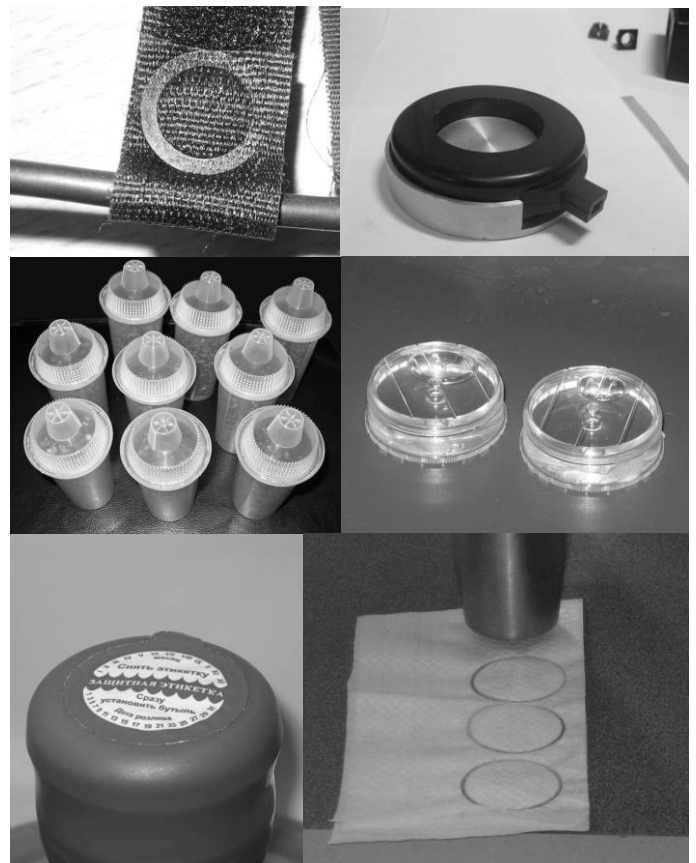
Виды изделий с кольцевыми сварными швами.
